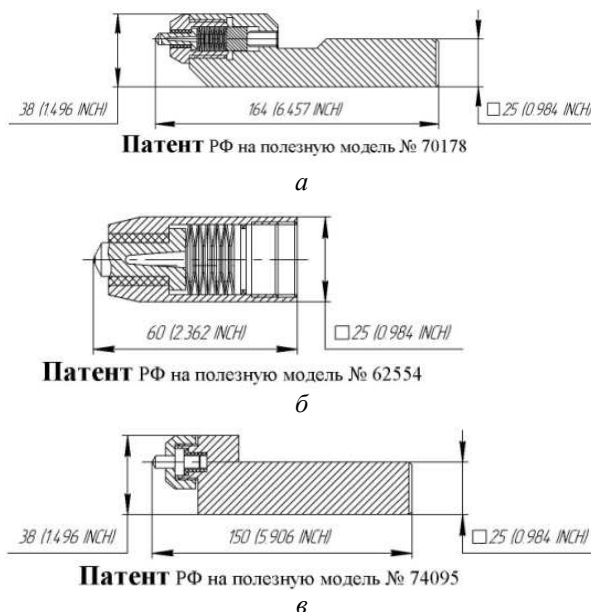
Выглаживающий инструмент для отделочной обработки деталей на станках с ЧПУ
